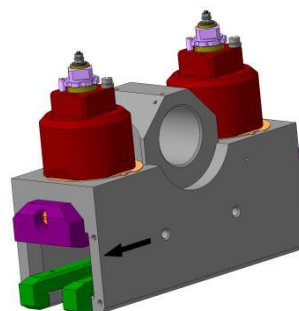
Общий вид тормозного башмака с установленными ПАДами
